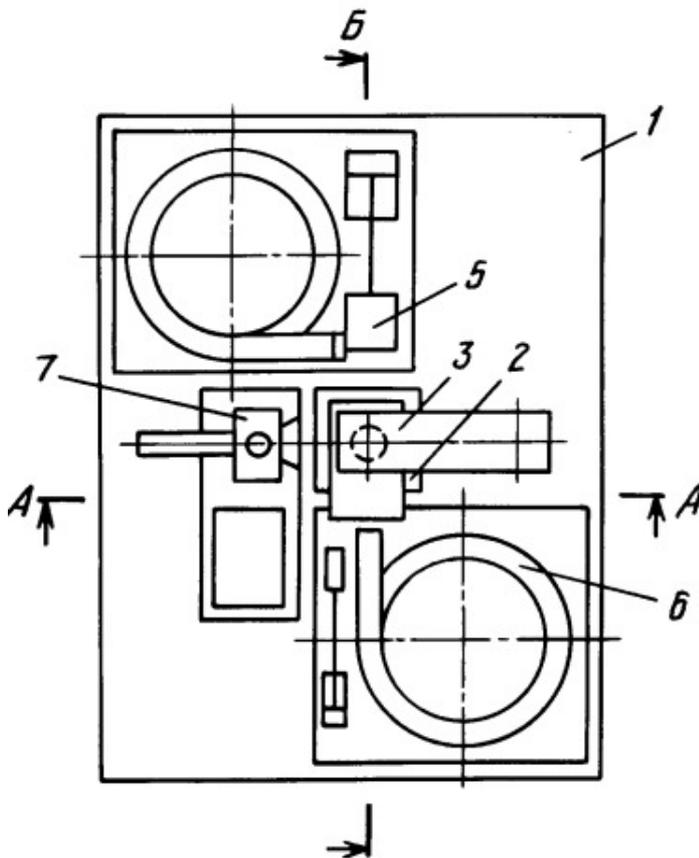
Автомат (А.С. 2043899), общий вид
